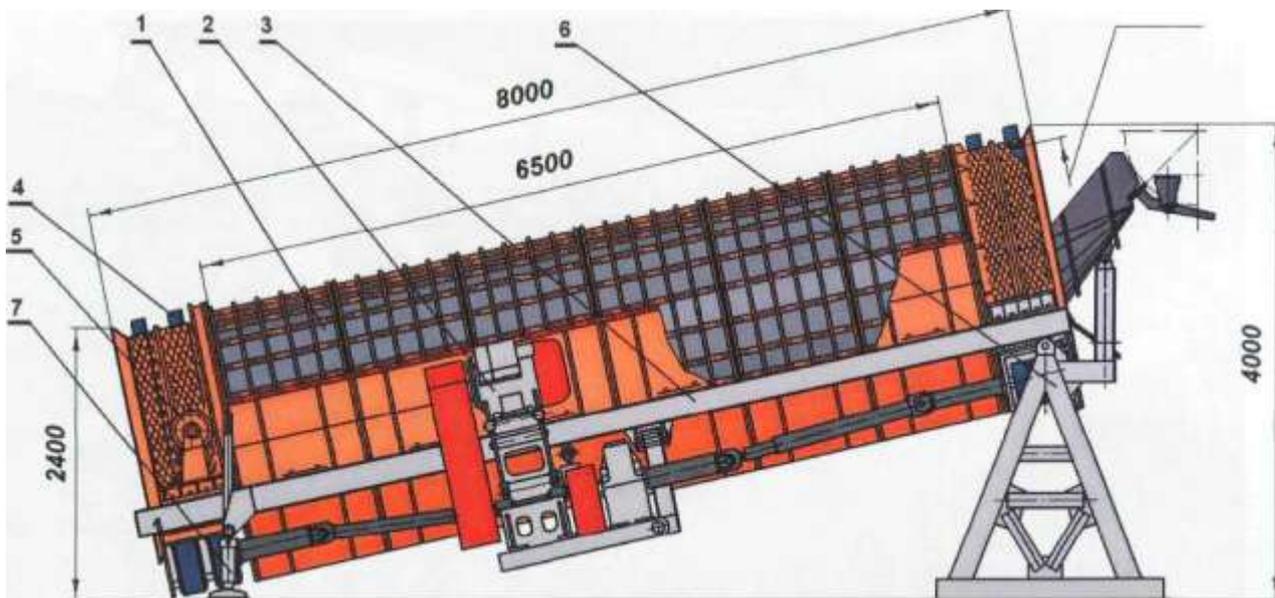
Схема конструкции и основные габаритные размеры грохота ГБК
